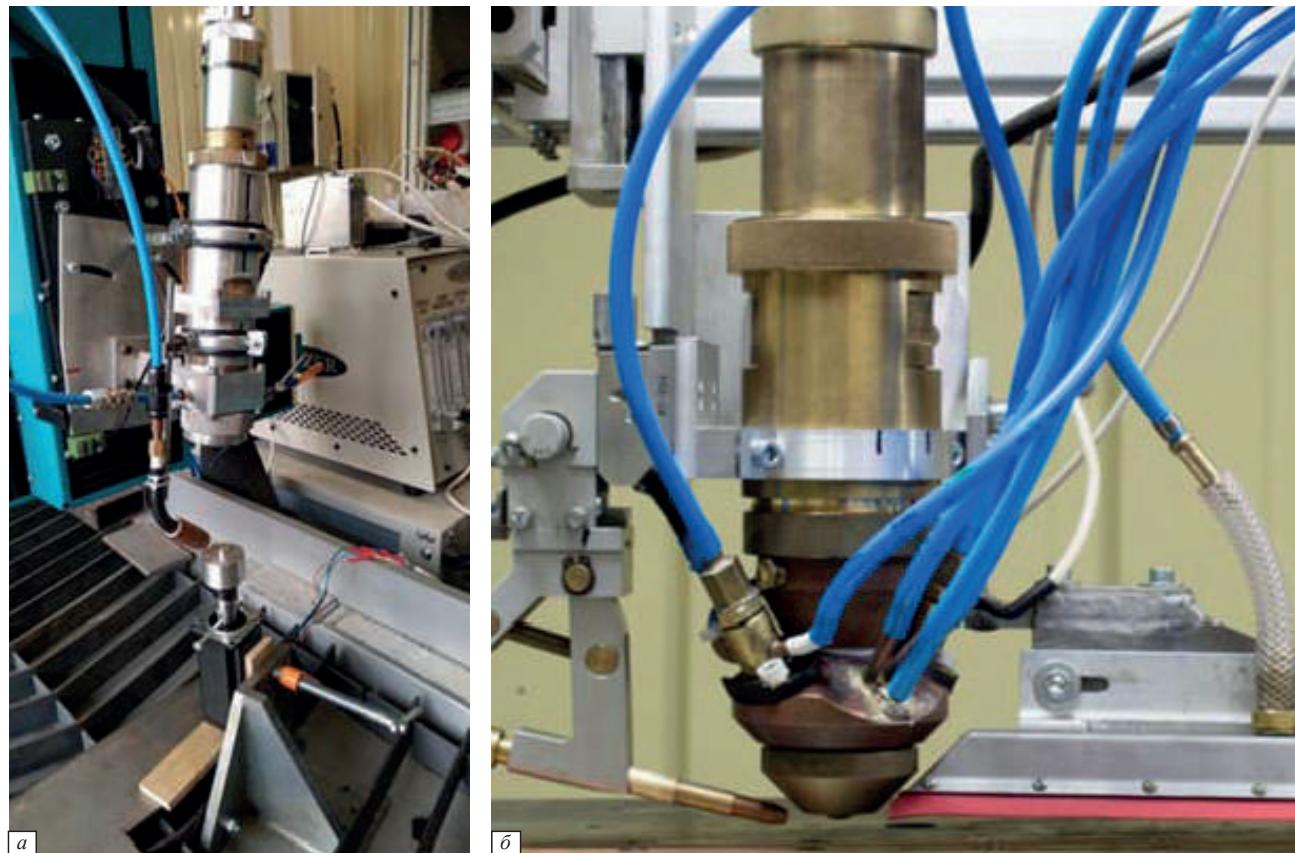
Створені в спільній лабораторії головки для лазерного (а) і гібридного лазерно-плазмового зварювання (б)
